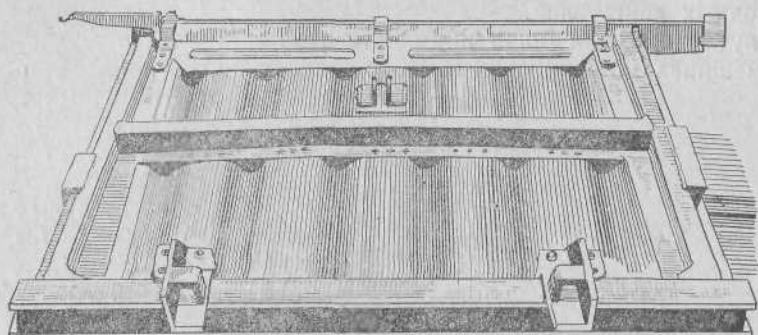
Усиленный сварной люк 62-тонного полувагона, изготовленный с применением гнутых профилей.
